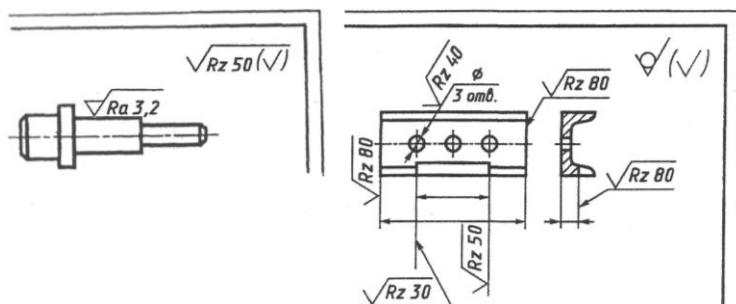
59. Обозначение шероховатости, одинаковой для части поверхностей изделия
